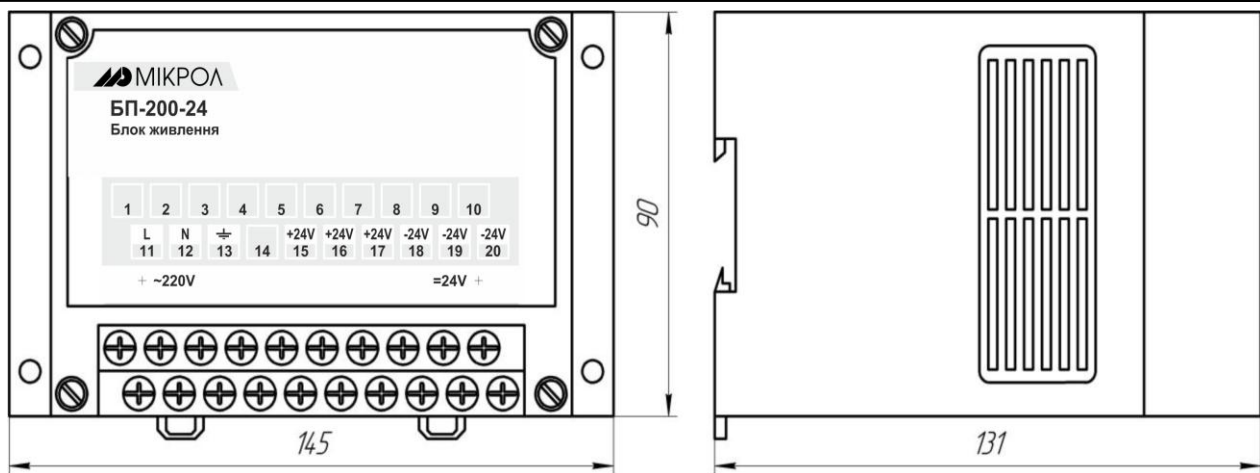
Зовнішній вигляд та габаритні розміри БП-200-24
